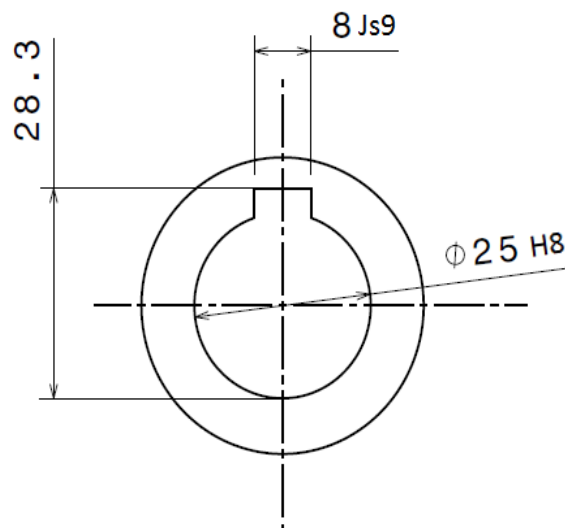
Esquema para maquinação da parte superior do acoplador flexível
